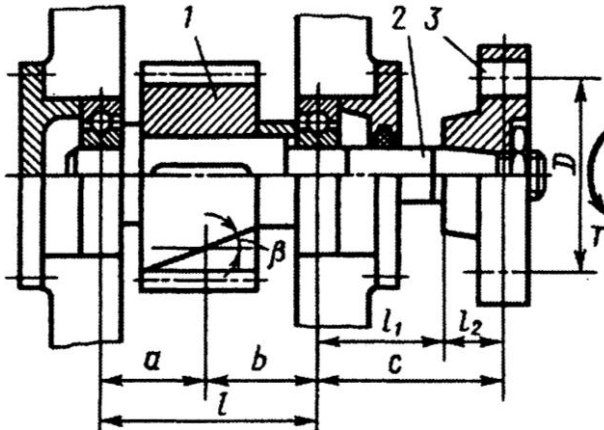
Вал с элементами, расположенными на нем: 1 – шестерня; 2 – вал; 3 – полумуфта
